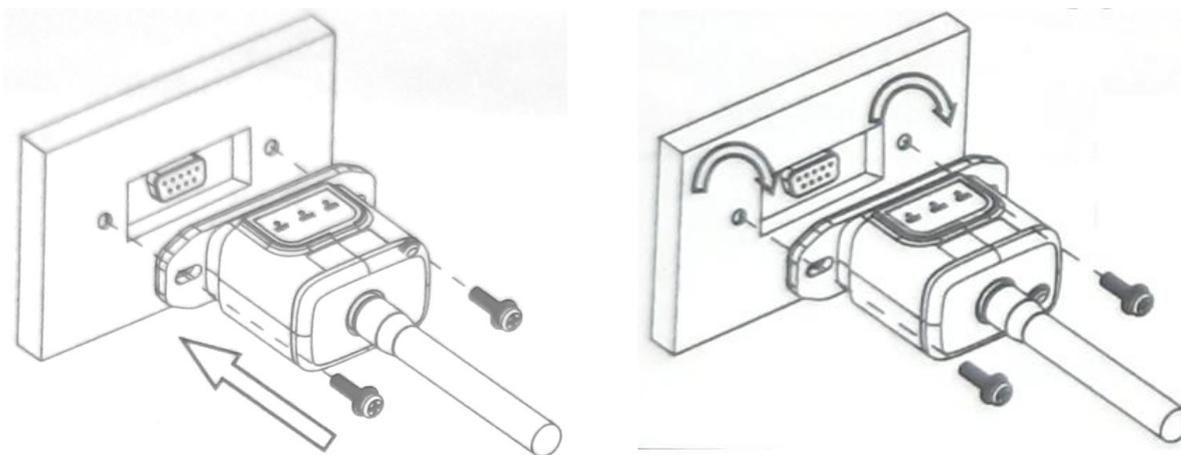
Inserimento e fissaggio della scheda wifi esterna
